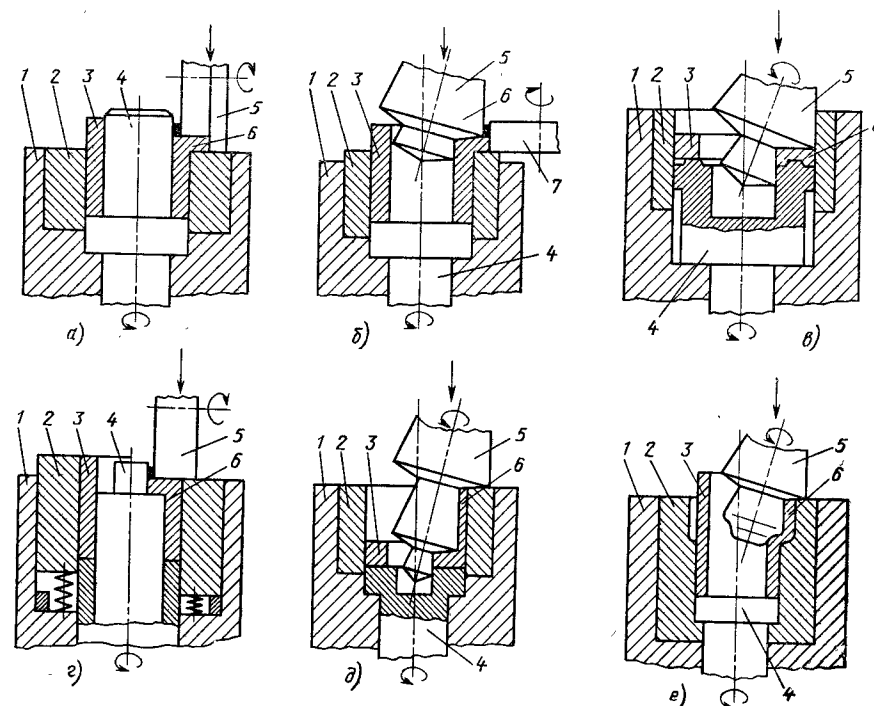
Основные схемы торцовой раскатки цилиндрическим и коническим деформирующими инструментами: а, б — высадка наружного бурта; в — раскатка кольца сложного сечения; г — высадка внутреннего бурта; д — обратное выдавливание; е — раздача; 1 — матричный блок; 2 — обойма матрицы; 3 — заготовка; 4 — оправка; 5 — раскатной цилиндрический валок; 6 — готовая деталь; 7 — ролик (в левой части схем изображена заготовка до деформации)
